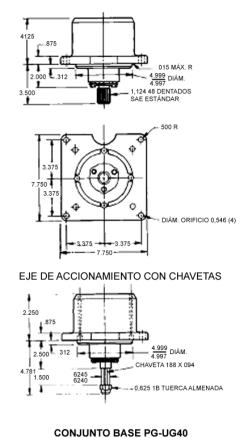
Plano esquemático de conjuntos base (No usar para construcción).
